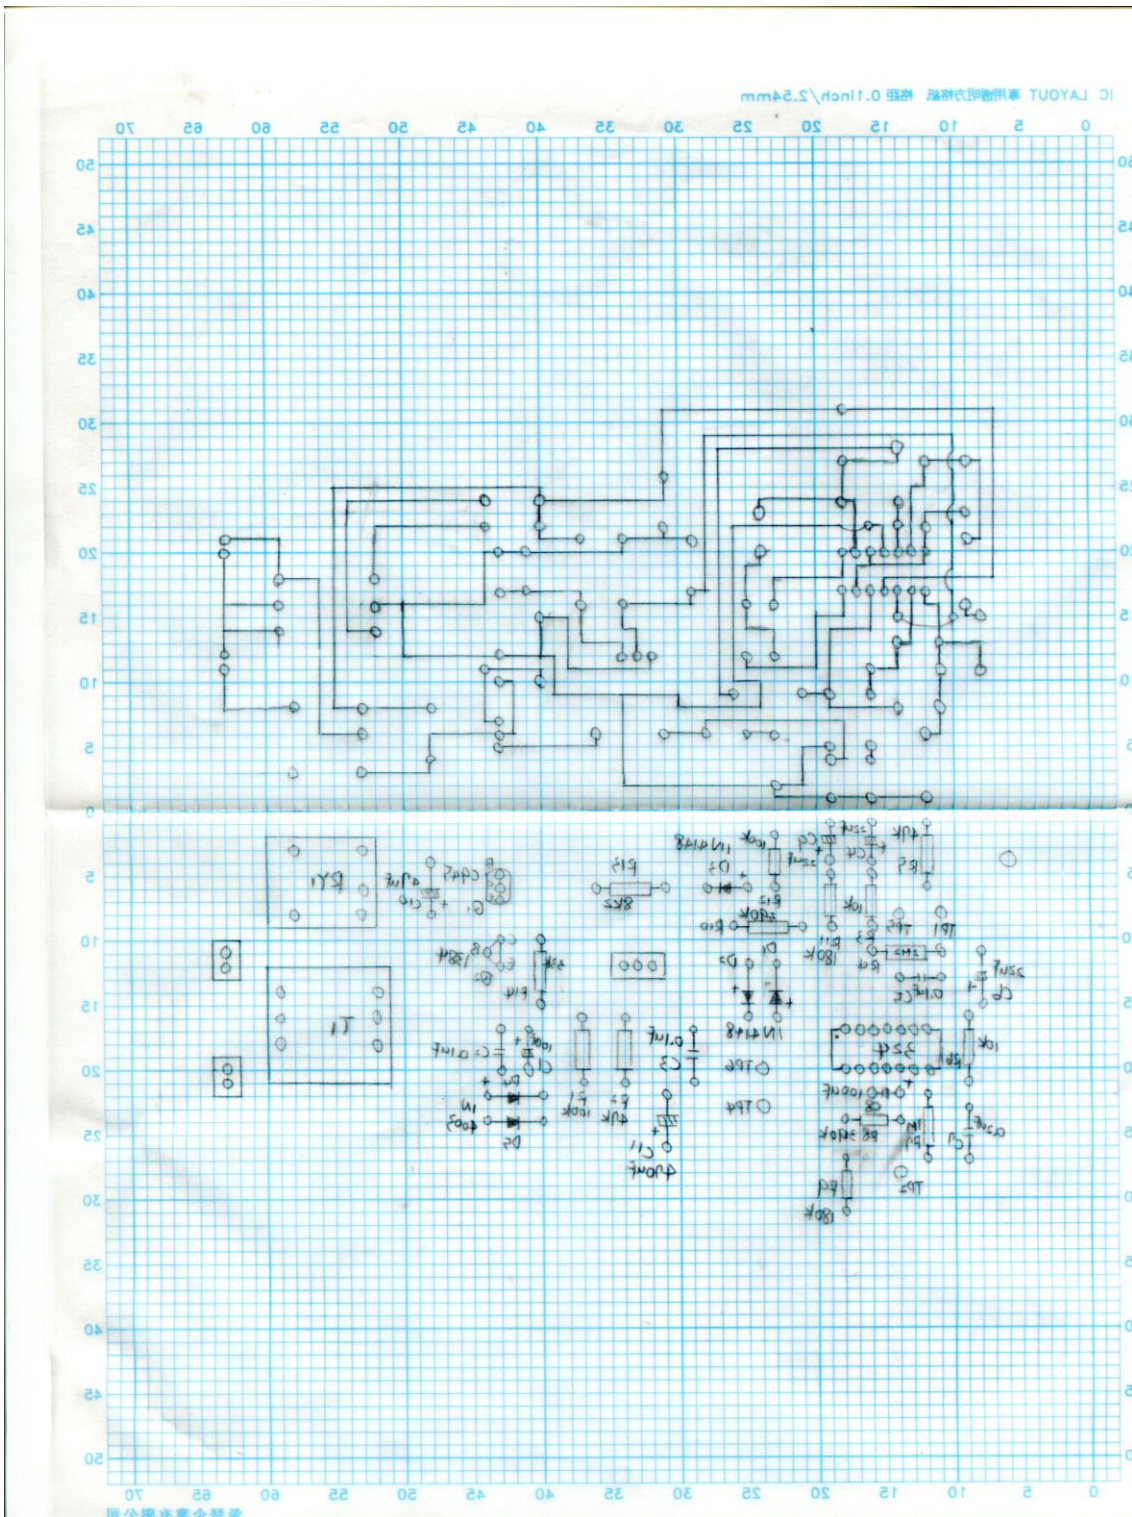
電路 Layout 圖焊接面與元件面
